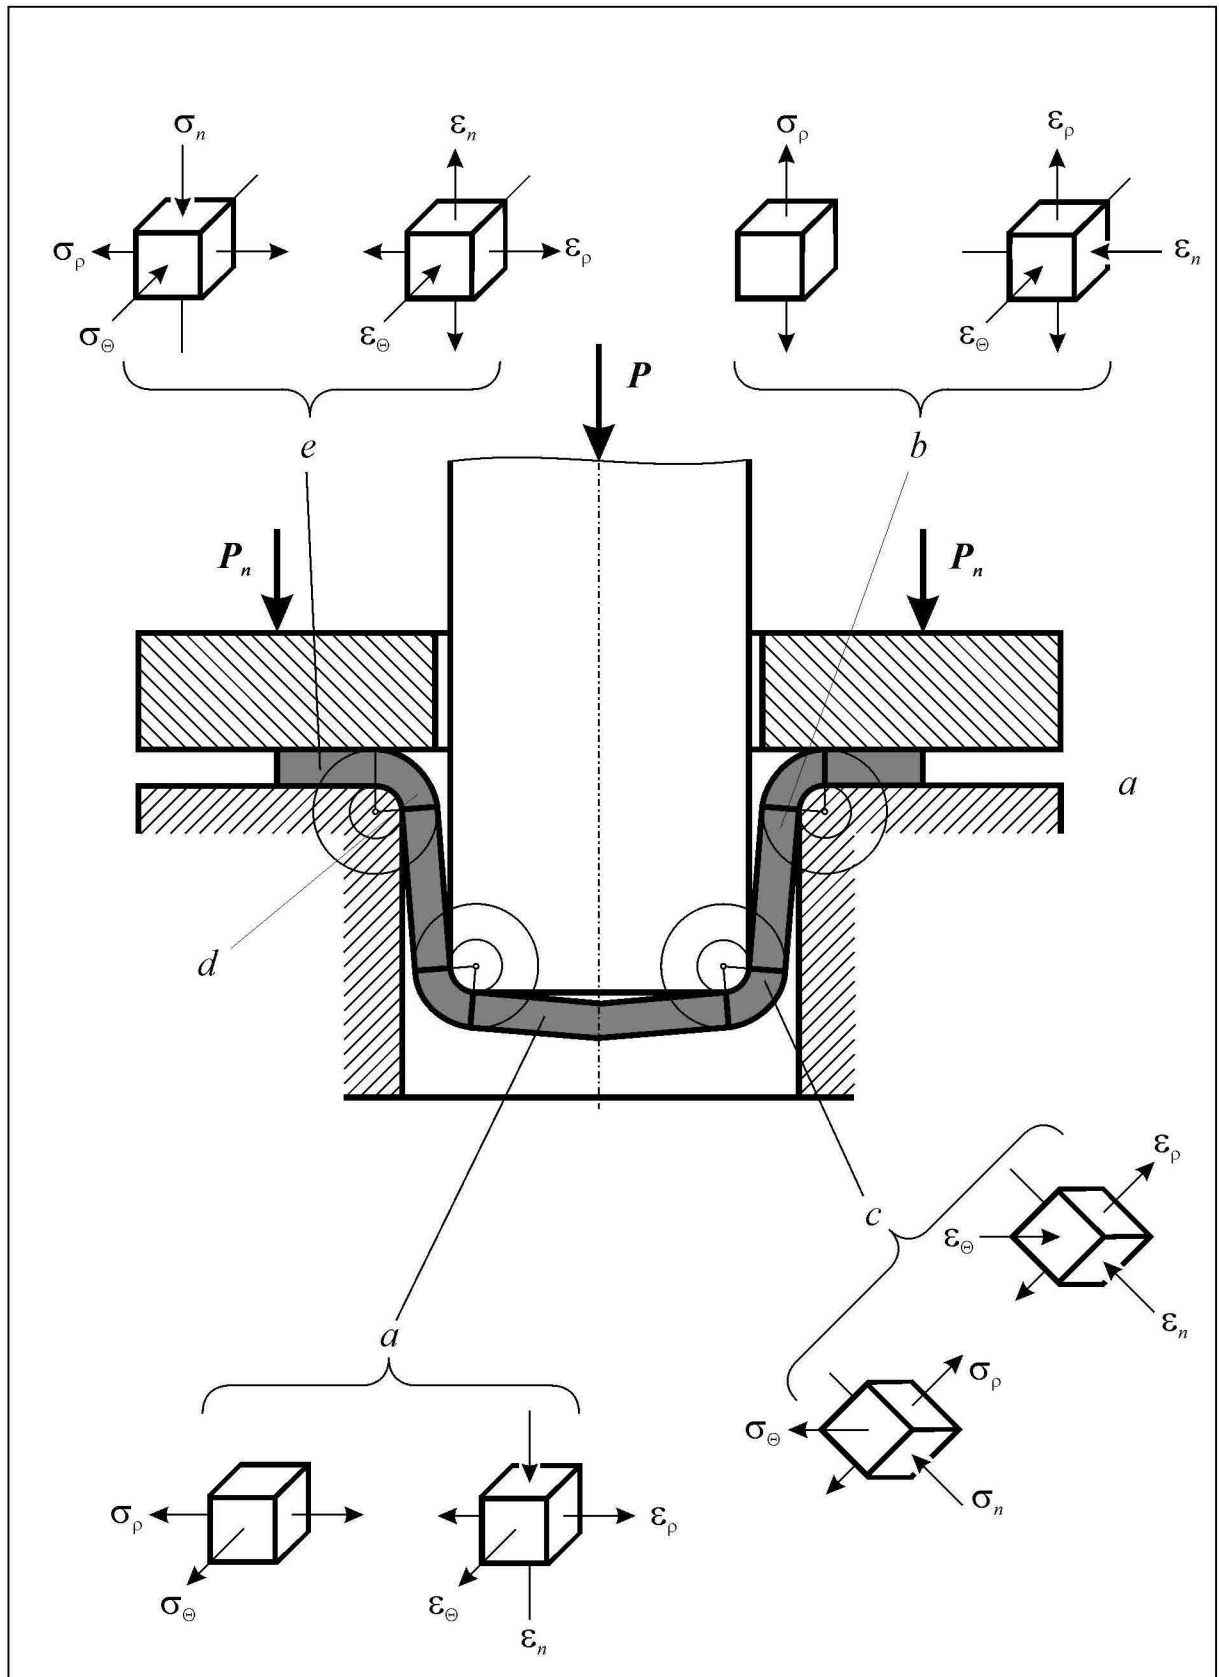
Схема напружено-деформованого стану заготовки при витягуванні з притиском фланця
